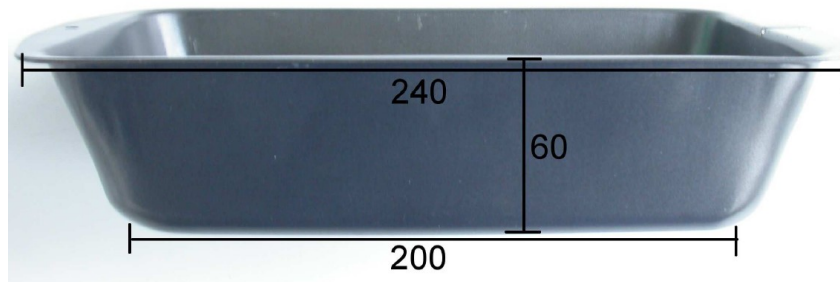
Rotationsformwerkzeug (Größenangaben in mm)
